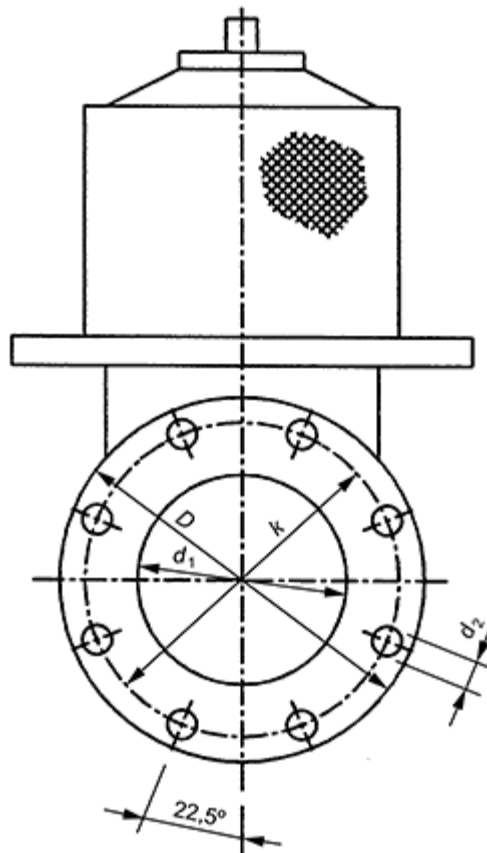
Присоединительные размеры сливного фланца для приемного клапана
